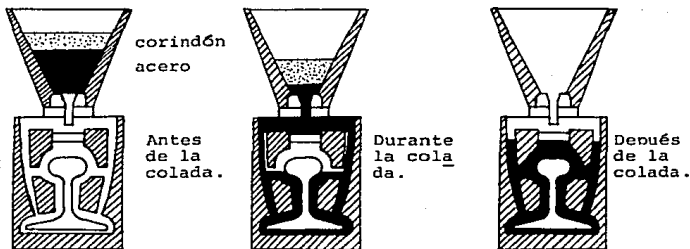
c Soldadura Aluminio - térmica.
